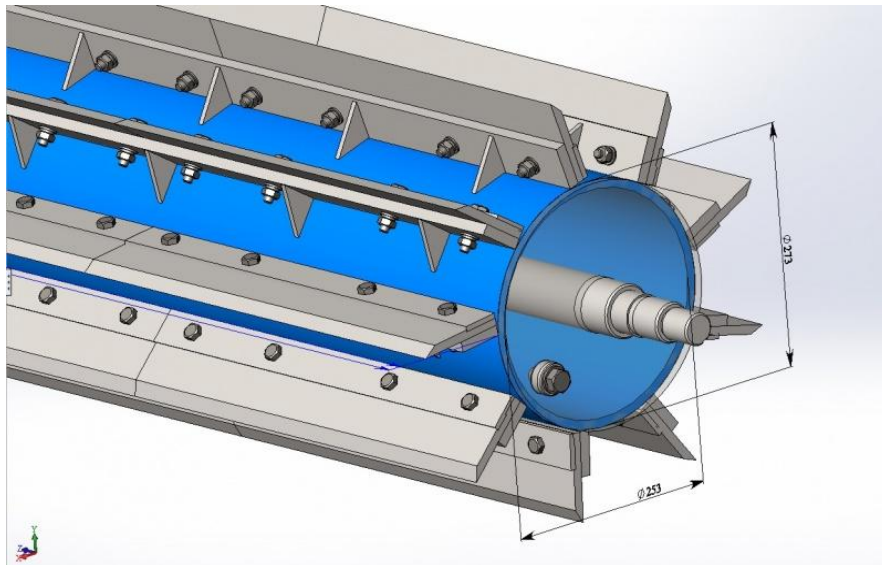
Типова конструкція реберчасто-планчатого катка
